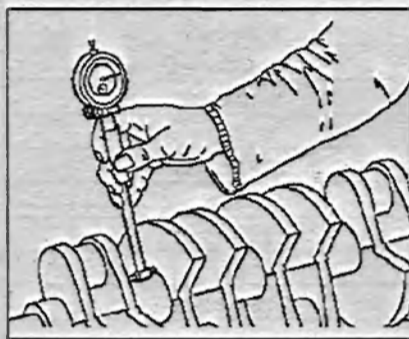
Измерение ширины коренной шейки коленчатого вала.
